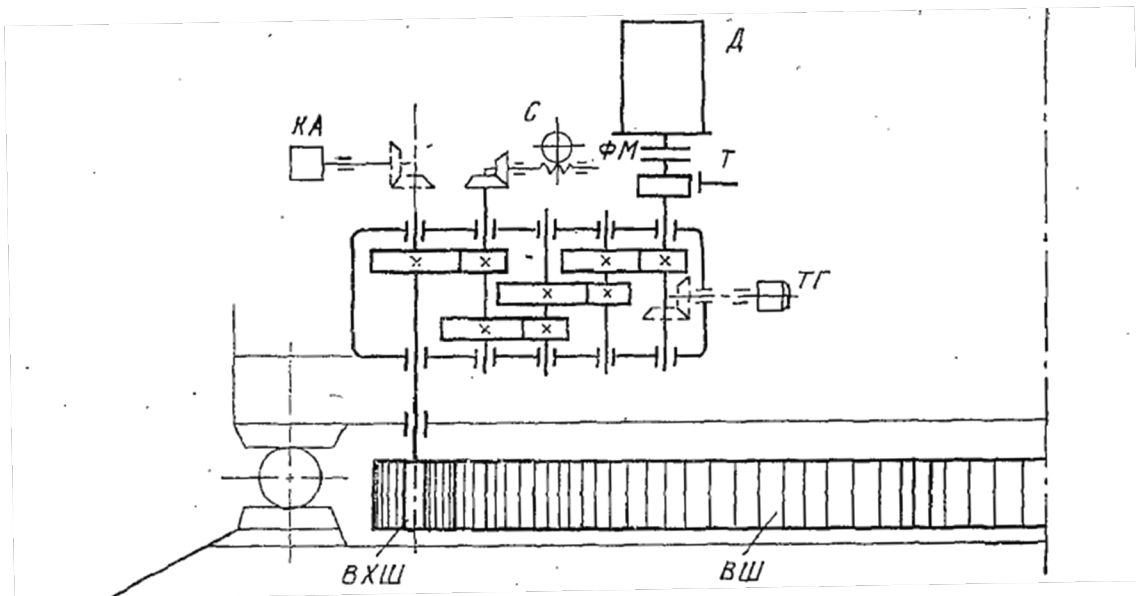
Схема одного приводу механізму повороту екскаватора
